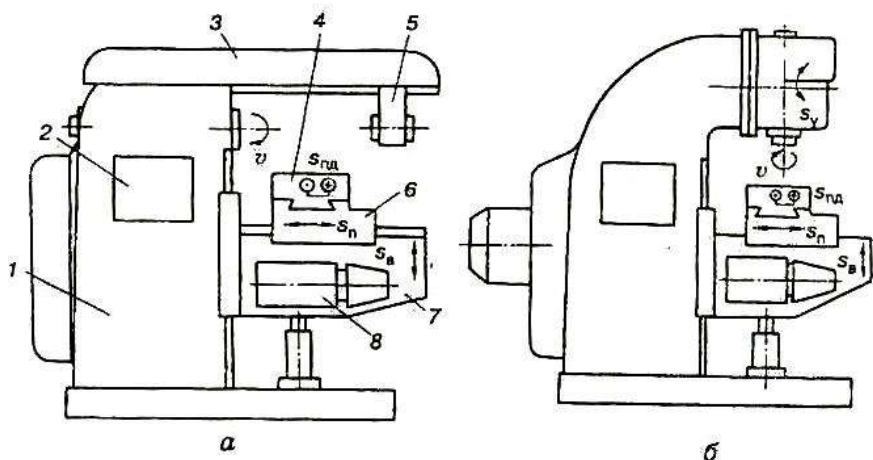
Консольны горизонтально-фрезерний (а) та вертикально-фрезерний (б) верстати
